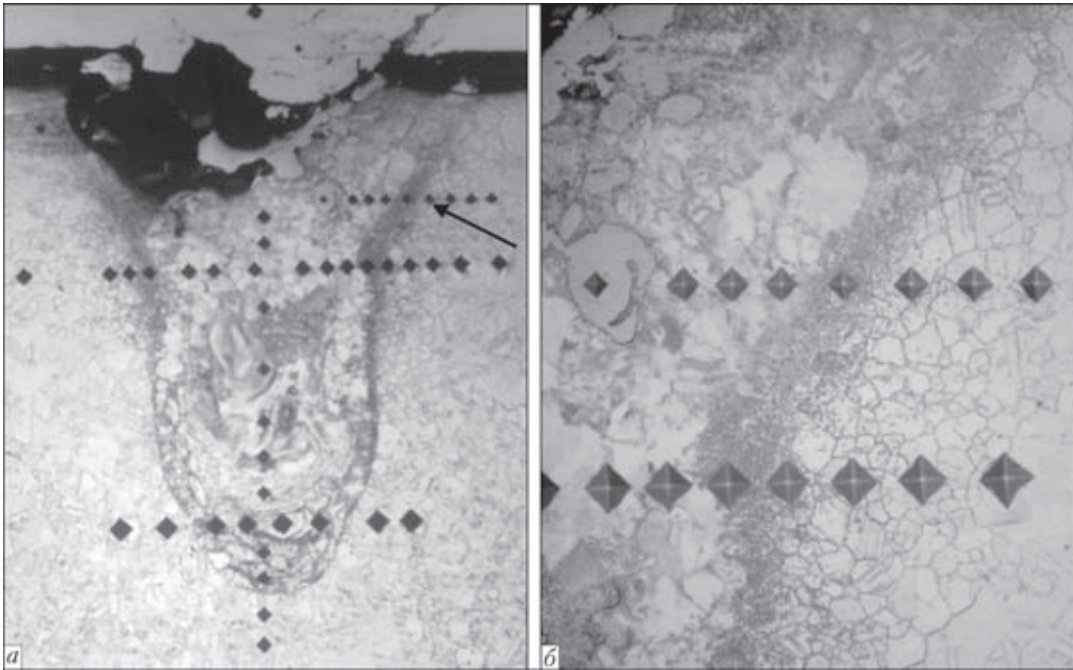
Макрошлиф сварного соединения с минимальным проплавлением: *a* — общий вид, латунь, $\times 250$; *б* — участок сплавления, $\times 800$
